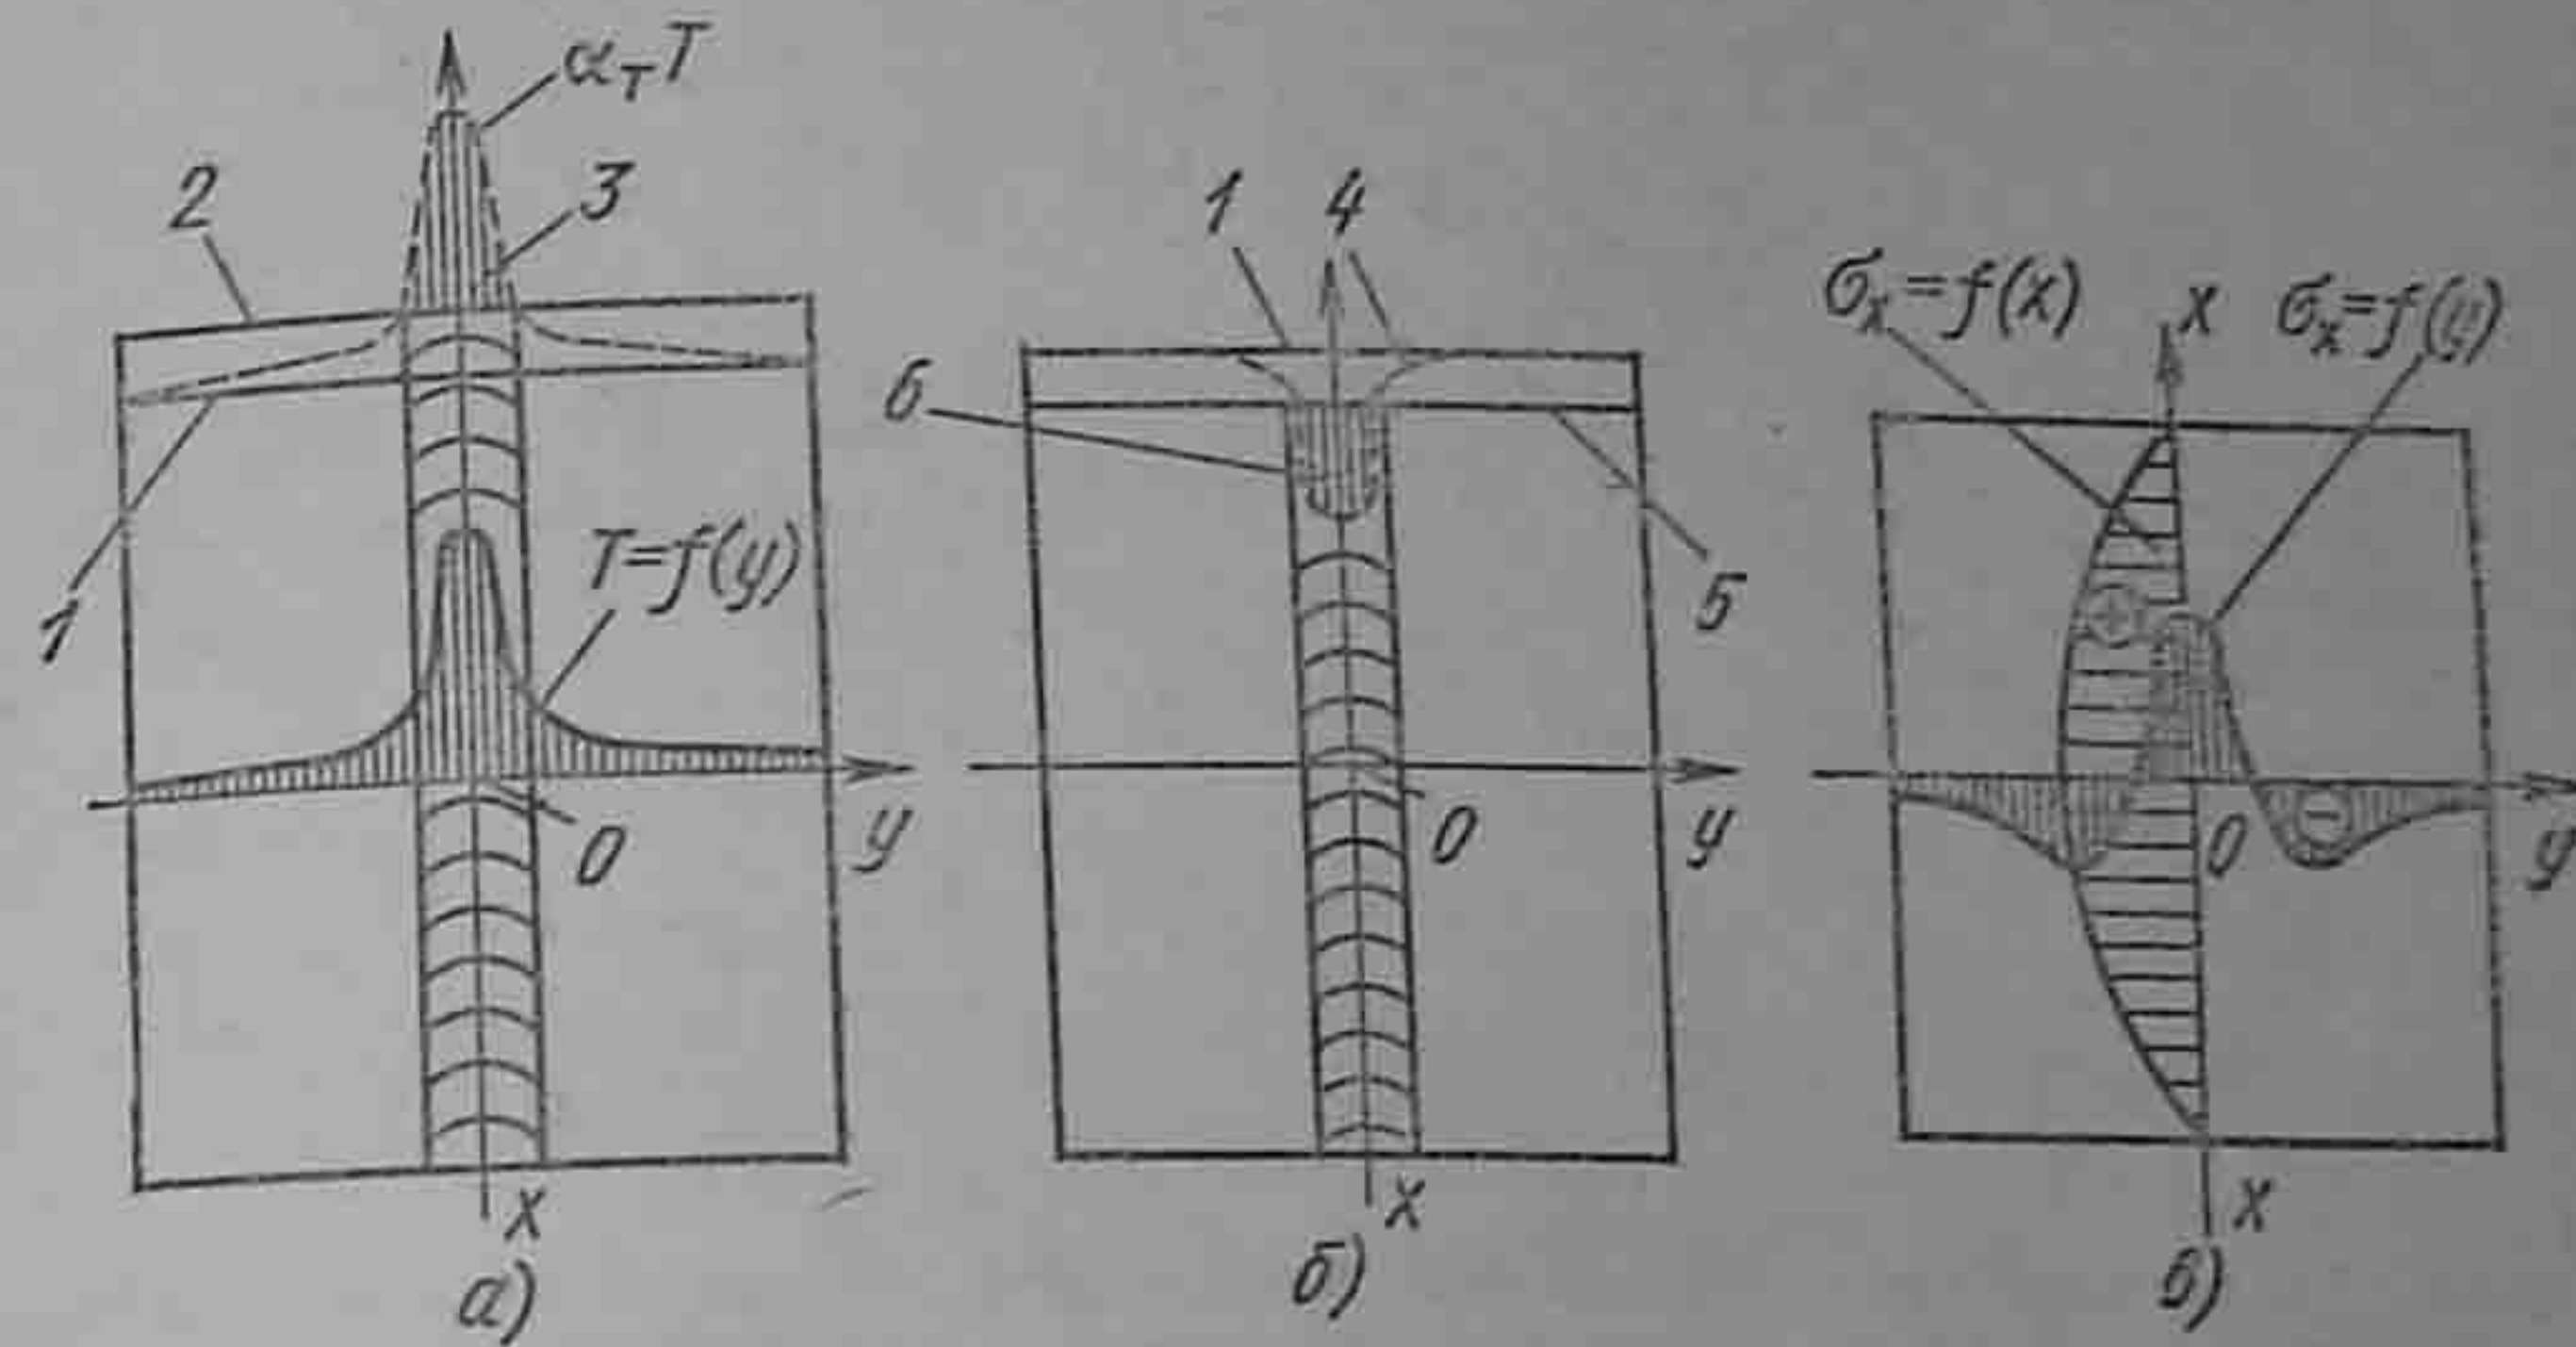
Процесс возникновения сварочных напряжений при сварке пластины встык:
